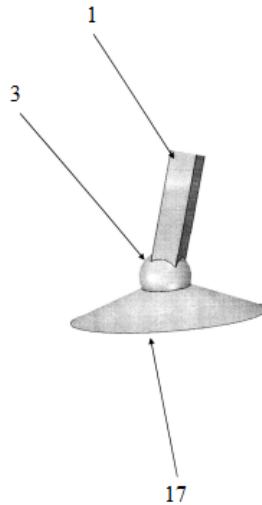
Варіант колісно-крокового рушія з опорними башмаками:
